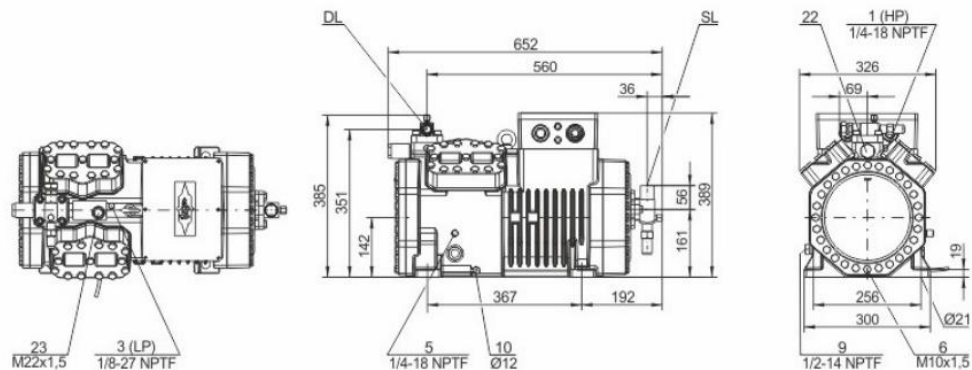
dimensioni del Compressore BITZER 4JTC - 15K
